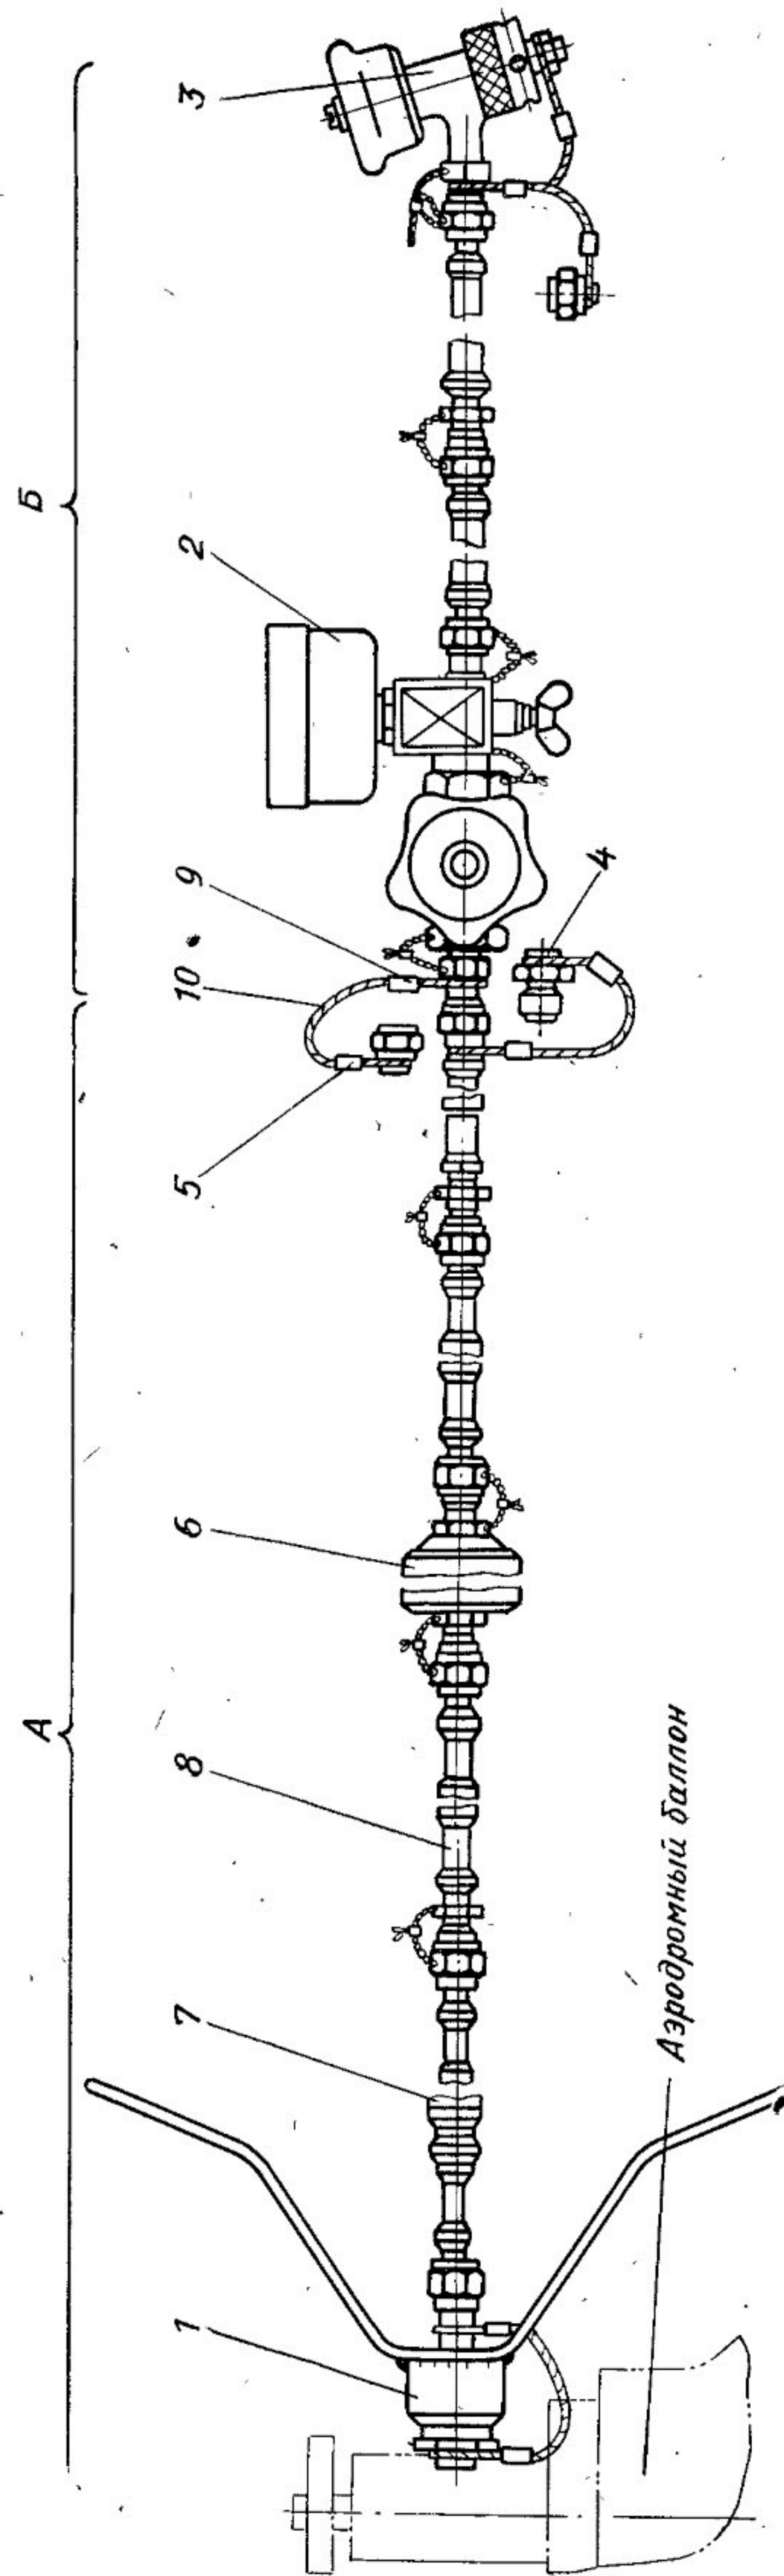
Приспособление для зарядки бортсети, гидроаккумуляторов, амортизационных стоек шасси и камер колес (вариант II сборки приспособления для зарядки бортсети):
